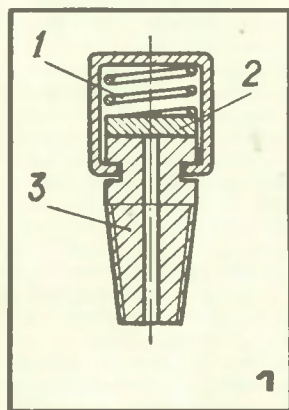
Пробка сапуна старой конструкции: 1 — пружина; 2 — диск; 3 — корпус.
